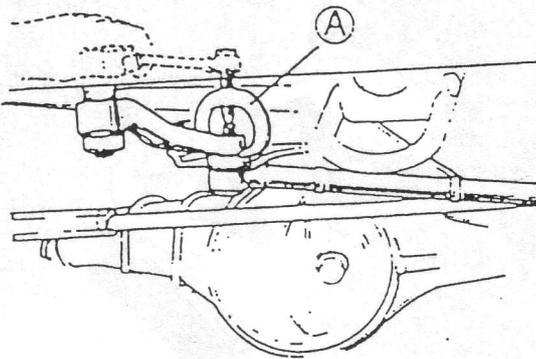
(A) Herramienta especial (Extractor del extremo de la barra de acoplamiento 09913-65210).
